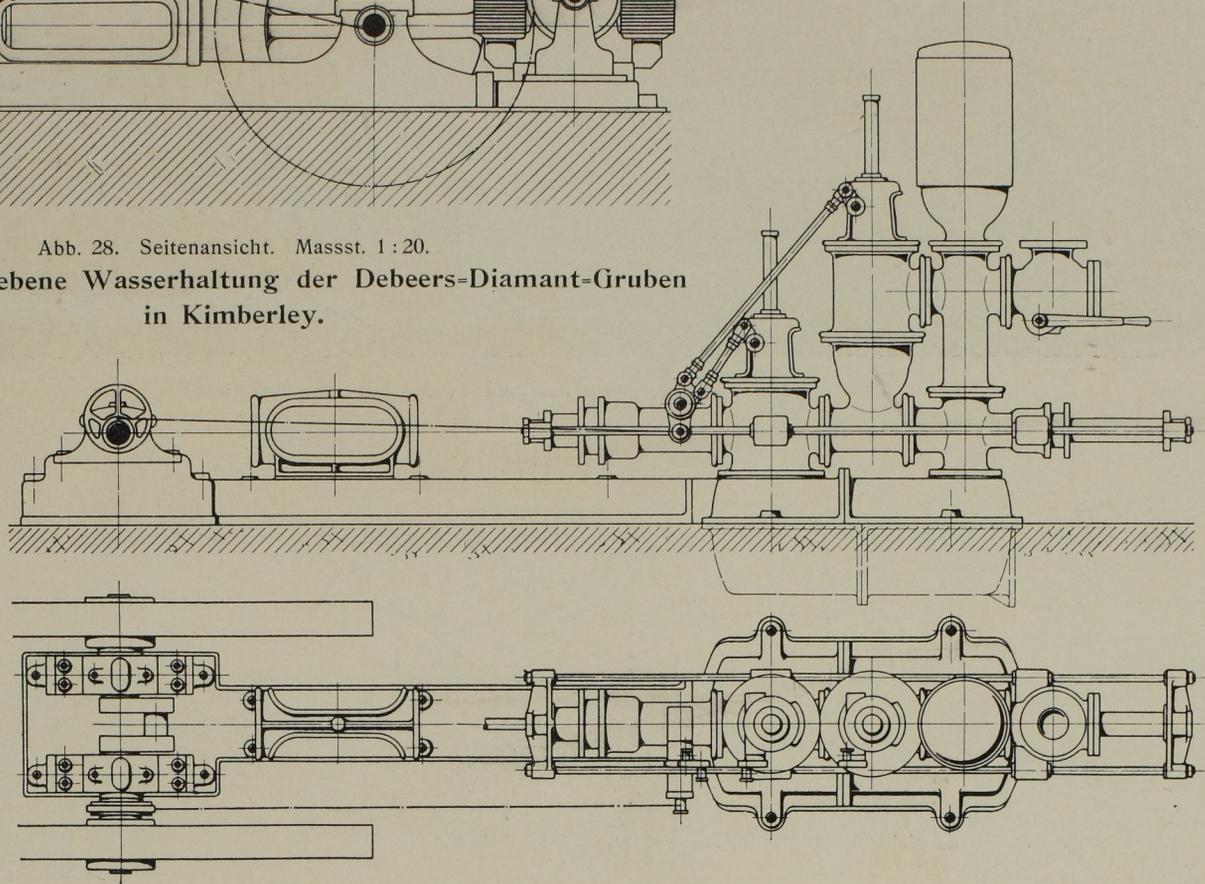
Grundriss und Seitenansicht der Pumpe. Massst. 1:32.
